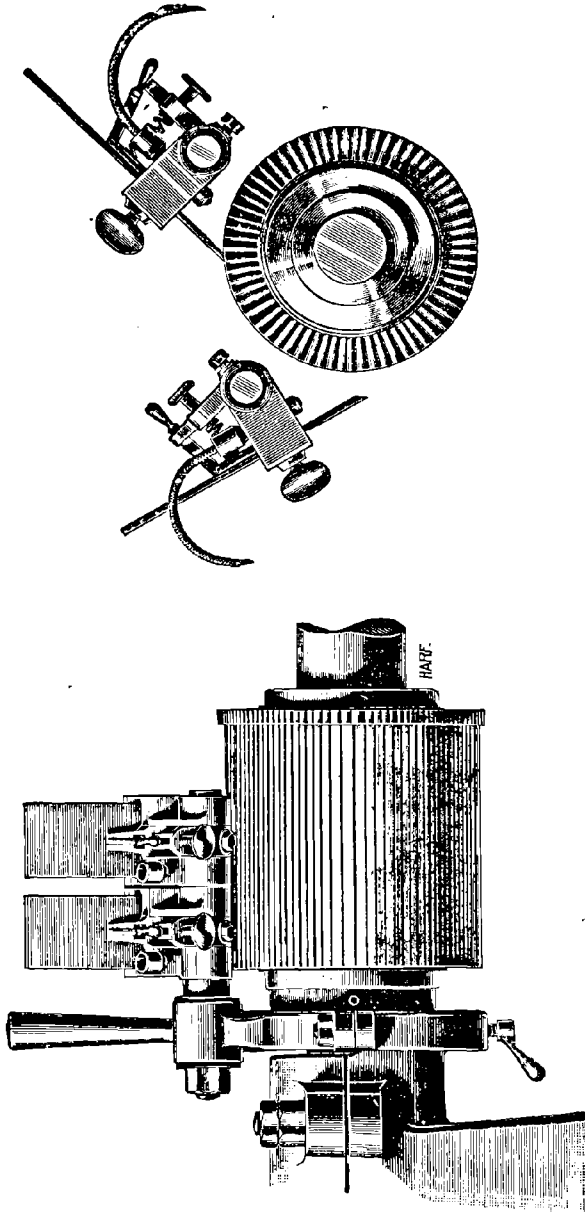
et 274. --- Collecteur et porte-balais de la machine Güntcher à 4 pôles.
